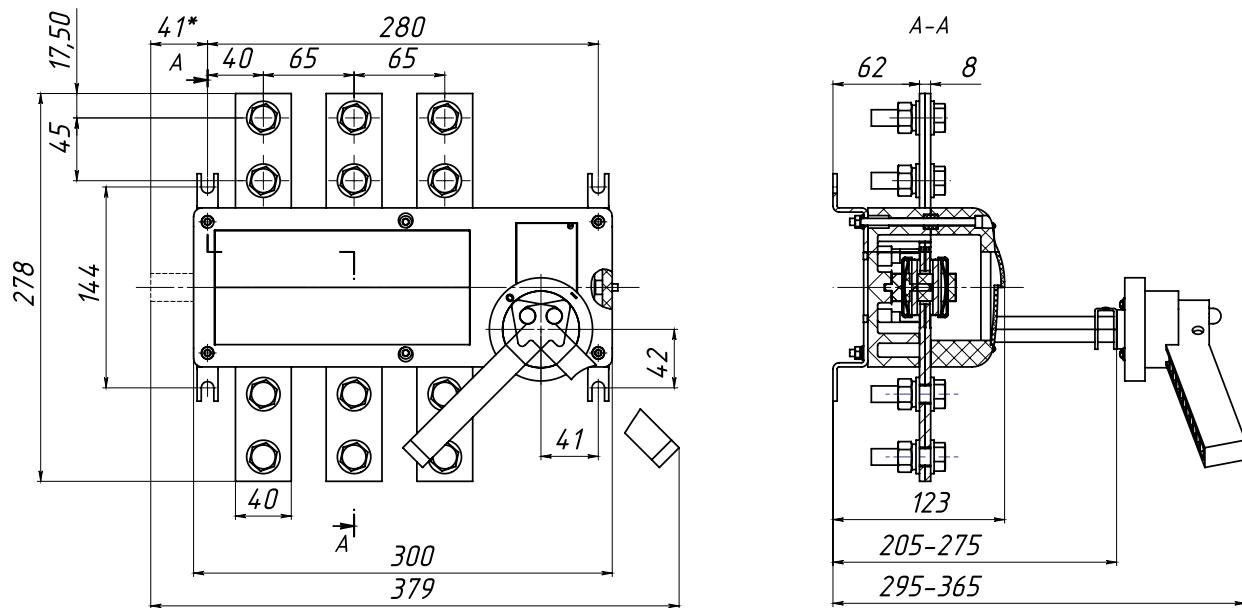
Выключатель-разъединитель ВНК-39-31130-32 УХЛЗ
